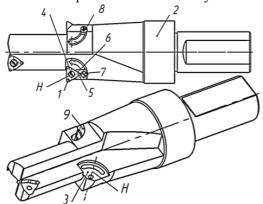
Конструкция ступенчатого сверла, обеспечивающая установку СМП на любой угол
